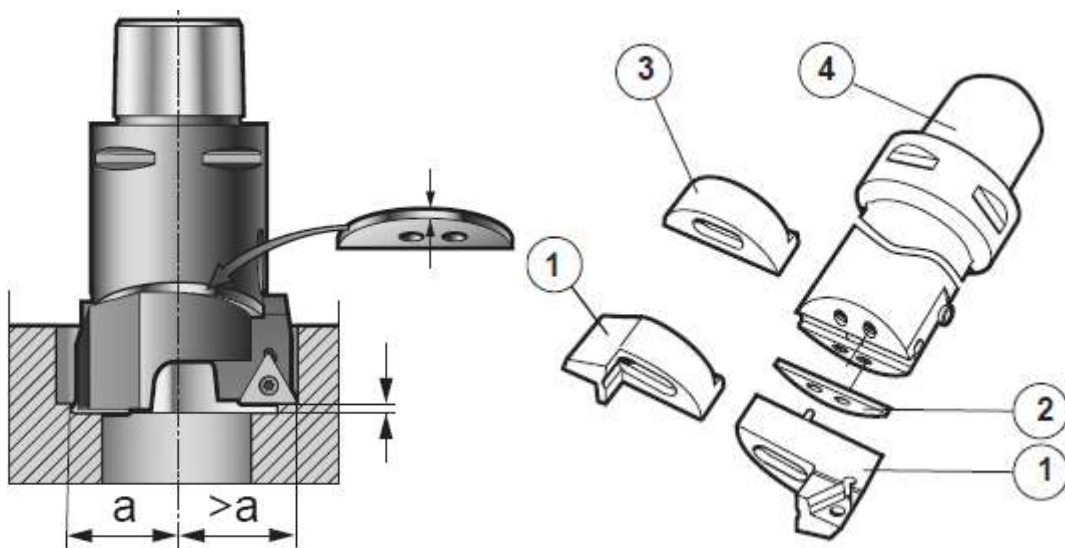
Типова конструкція різцевої головки для ступеневого розточування із регулюванням проставкою: 1 – різцева вставка; 2 – проставка; 3 – заглушка; 4 – корпус
